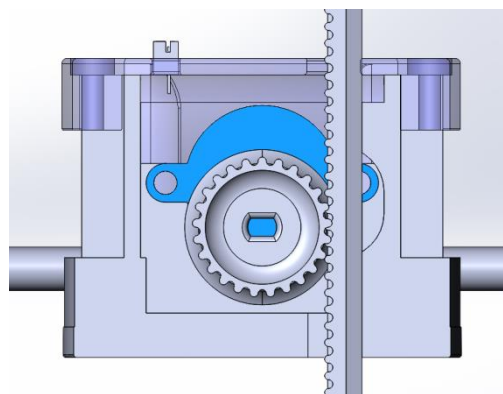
Сопряжение рейки рабочего органа с зубчатым колесом каретки
